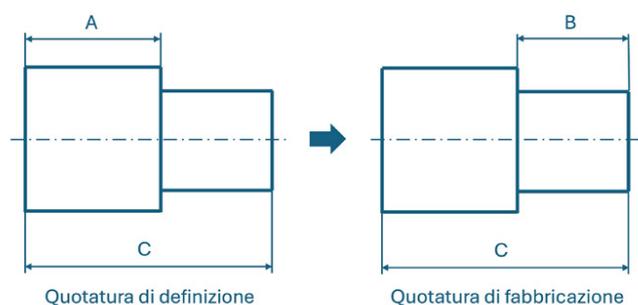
Modifica della quotatura del disegno per scopi di fabbricazione (trasferimento di quota)
